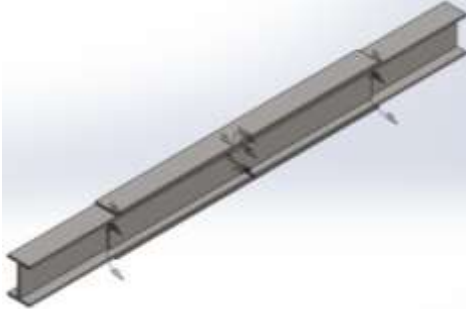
Робоче креслення зварної сталеві балки
